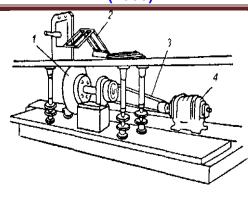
Механическая пила для резки стеклянных трубок: 1—стальной диск с режущей кромкой; 2—защитная рамка; 3—ременная передача; 4—электродвигатель.
